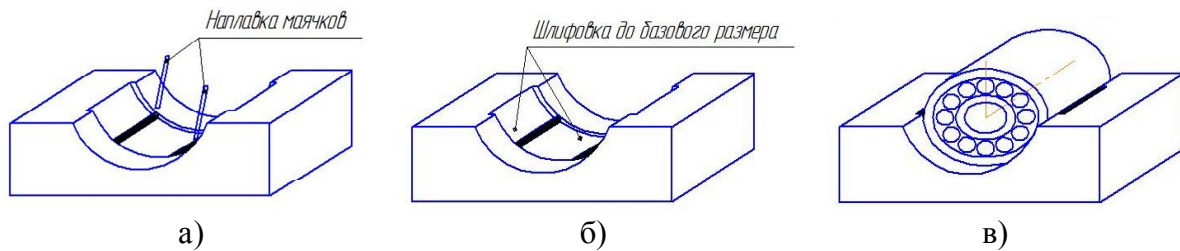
Подготовка и расположение установочных маячков, нанесение материала и установка подшипника в проектное положение: а – наплавка маячков; б – шлифовка до базового размера; в – установка подшипника
